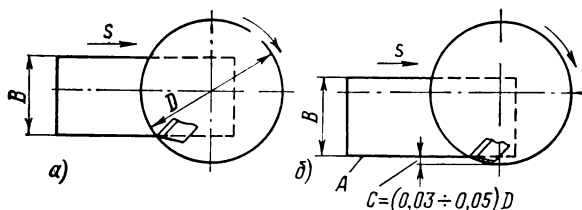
Установка заготовки относительно оси фрезы при обработке стали и чугуна:
